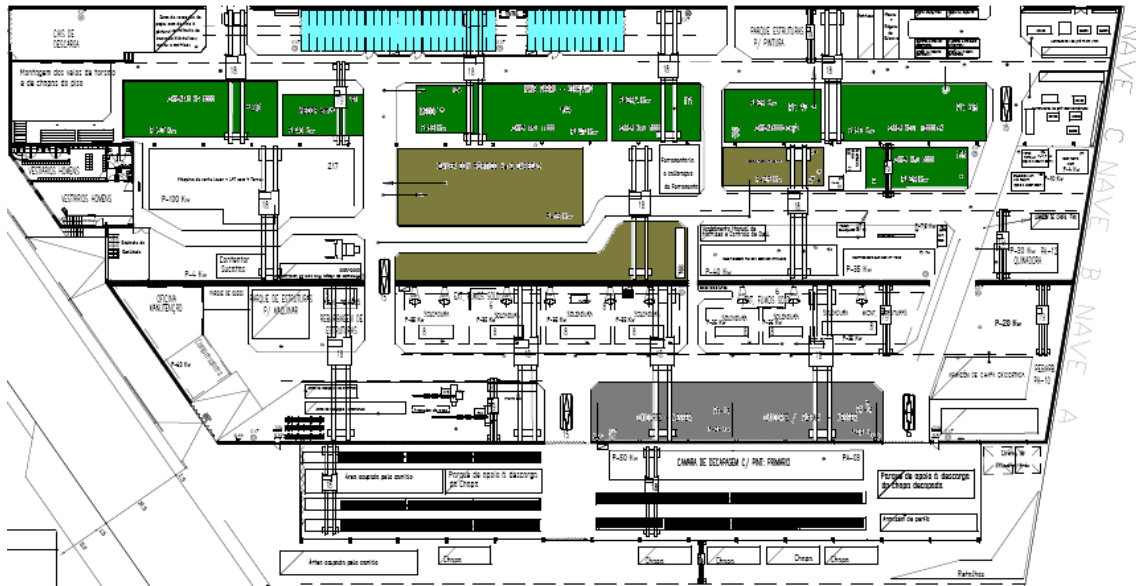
Layout Oxisol: Cinza – Oxi-Corte; Castanho - Soldadura; Verde - Maquinagem CNC; Azul - Pintura.
